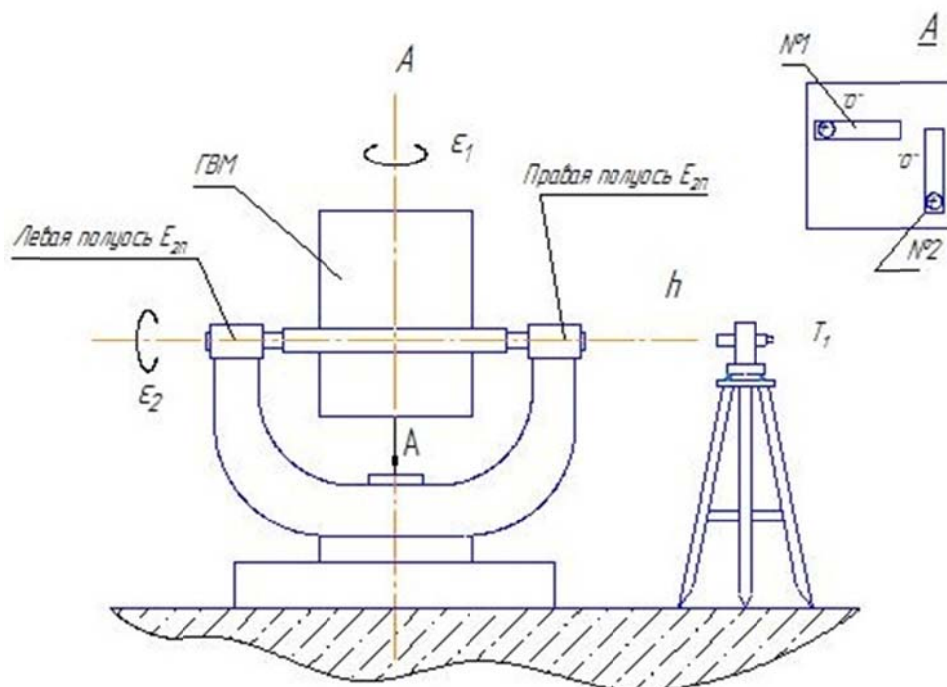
Схема ОПУ СМ-690 и обозначение базовых элементов
